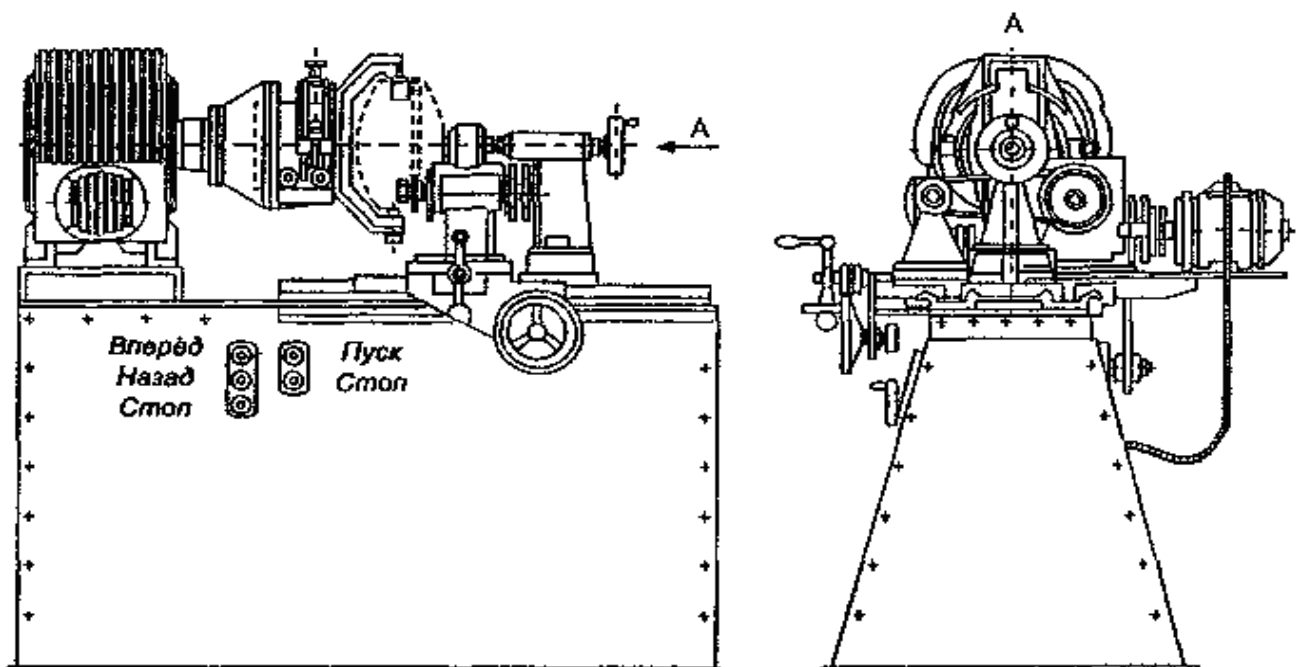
Верстат для розрізання кожуха мотор-компресора холодильного агрегату
